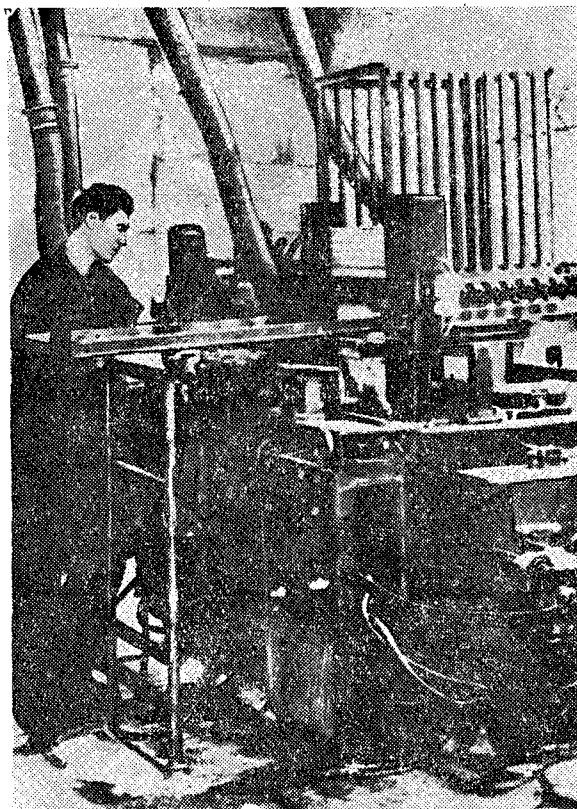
Контейнерный питатель конструкции ЛТА-СКБ.
